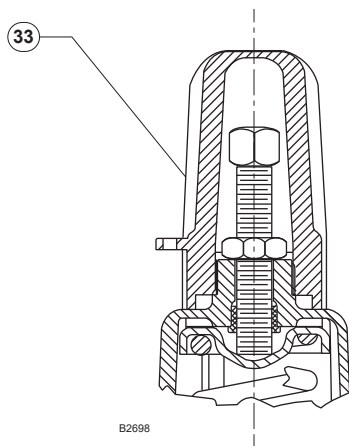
Дополнительный защитный колпак [только для вентиляционного отверстия корпуса пружины с резьбой 6,4 мм / 1/4 дюйма]
